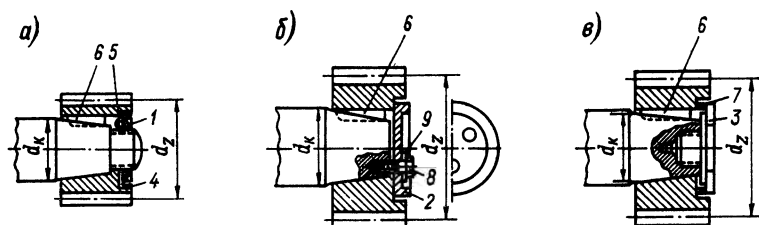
Способы крепления малого зубчатого колеса на конце вала двигателя: а — крепление кольцевой гайкой; б — крепление шайбой и винтами; в — крепление винтом
